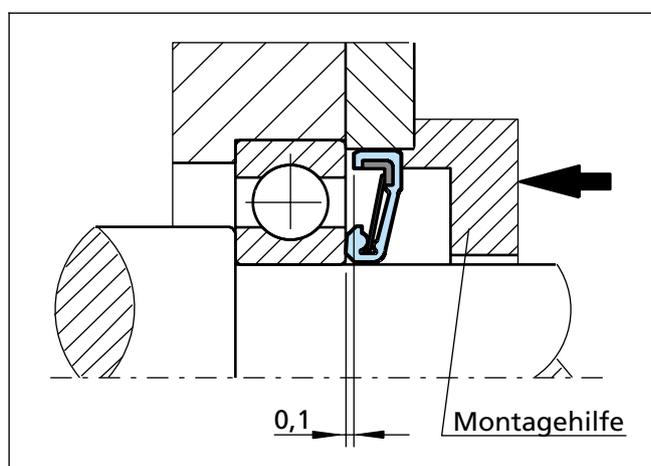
Einbau der Axial-Wellendichtung mit Montagehilfe
